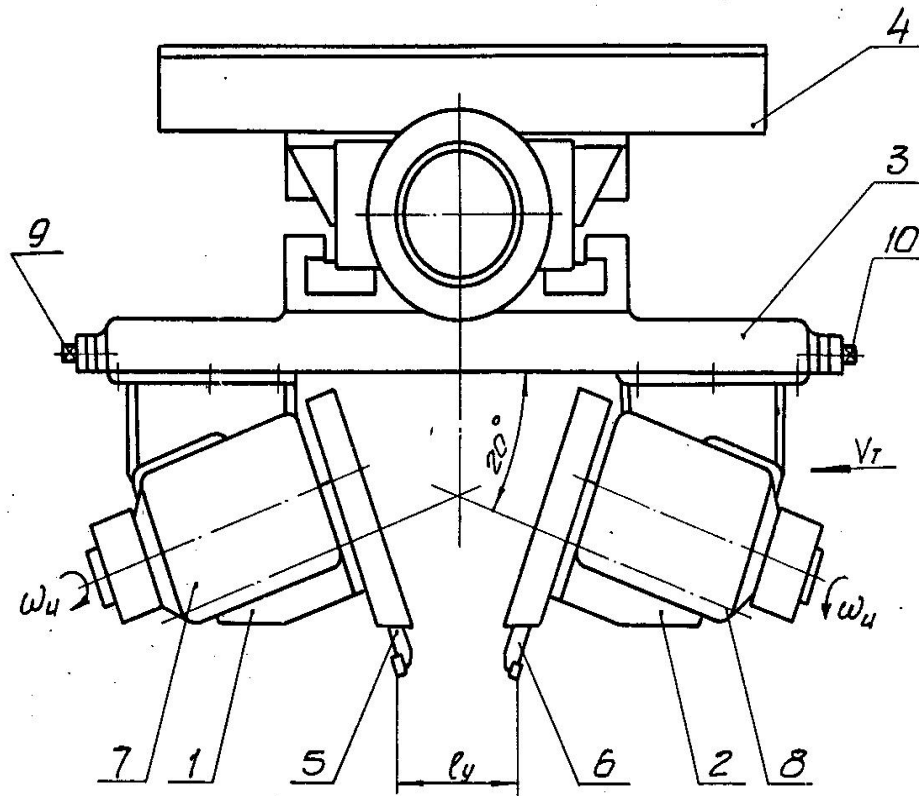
Принципова конструкція двошпindelного спеціального супорта до зубофрезерного верстата мод. 5343
